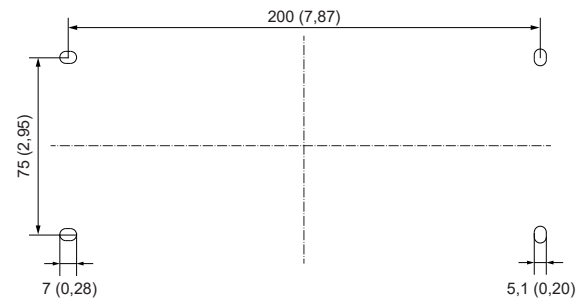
Bohrschablone für Edelstahl-Gehäuse
